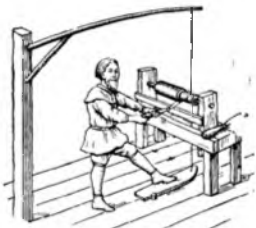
Токарный станок, приводимый в движение ногой (1400)
